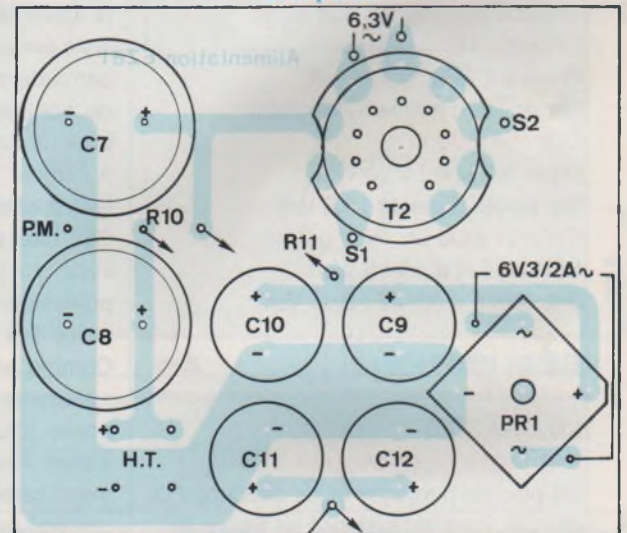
le support de tube et le pont sont soudés côté pistes
